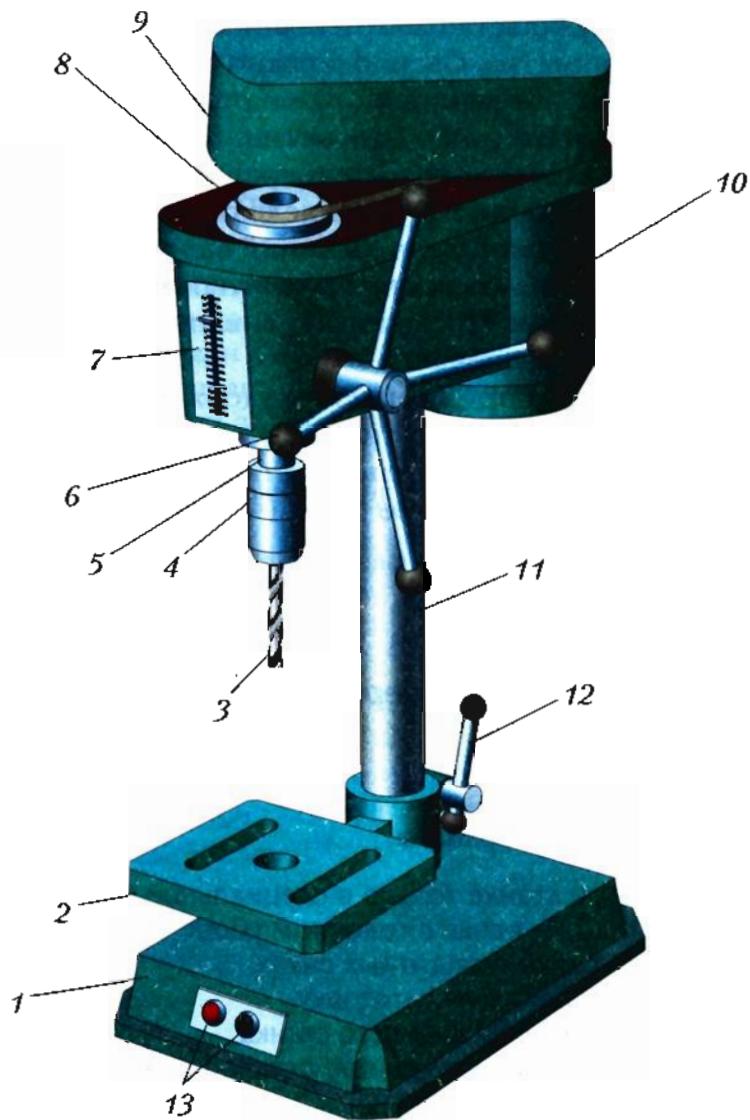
Сверлильный станок: 1 – основание (станина); 2 – рабочий стол; 3 – сверло; 4 – патрон; 5 – рабочий вал; 6 – рукоятка подачи сверла; 7 – шкала глубины сверления; 8 – шкив с ремнем; 9 – защитный кожух; 10 – электродвигатель; 11 – колонна; 12 – стопор; 13 – пусковые кнопки
